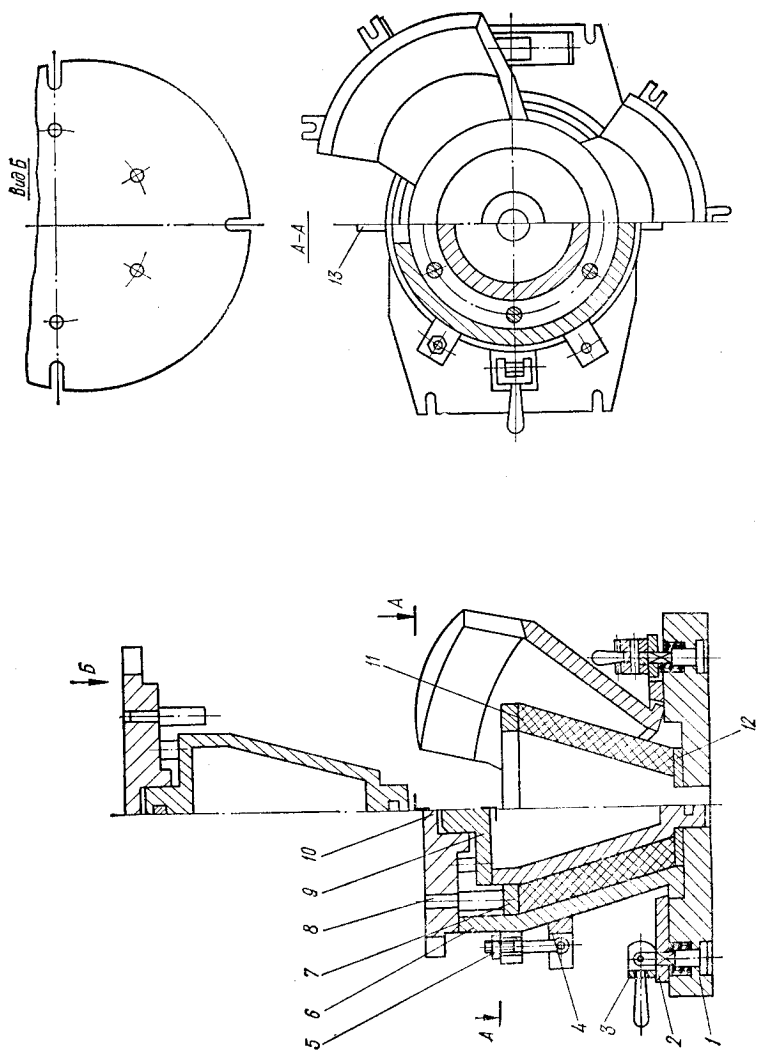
Конструктивное оформление пресс-формы для изделий типа «конус».
